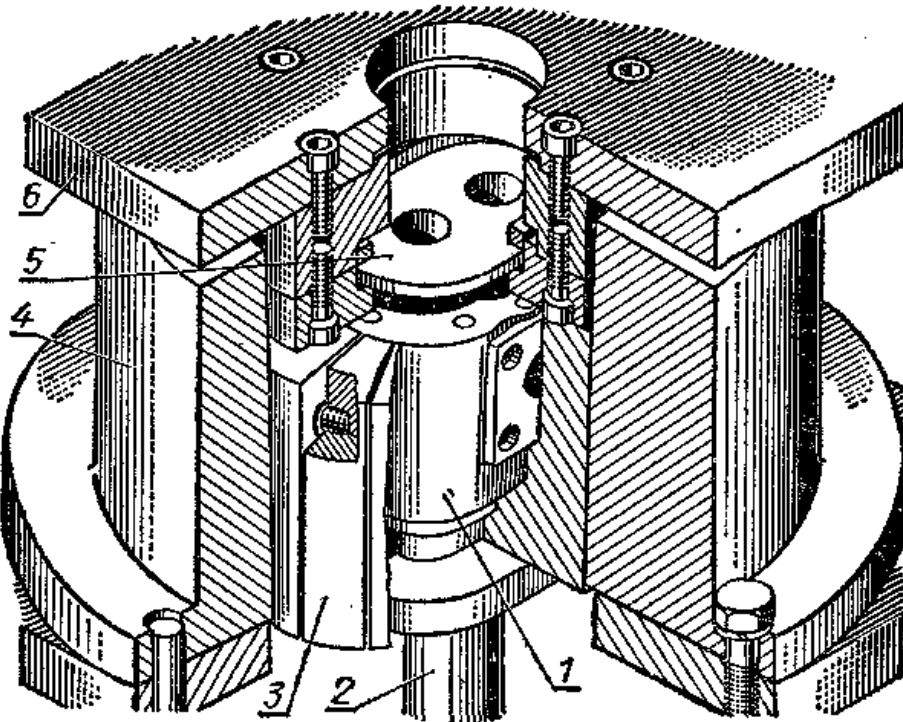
Пристосування для обтиснення корпусу насоса а процесі гарячого пластичного деформування:
